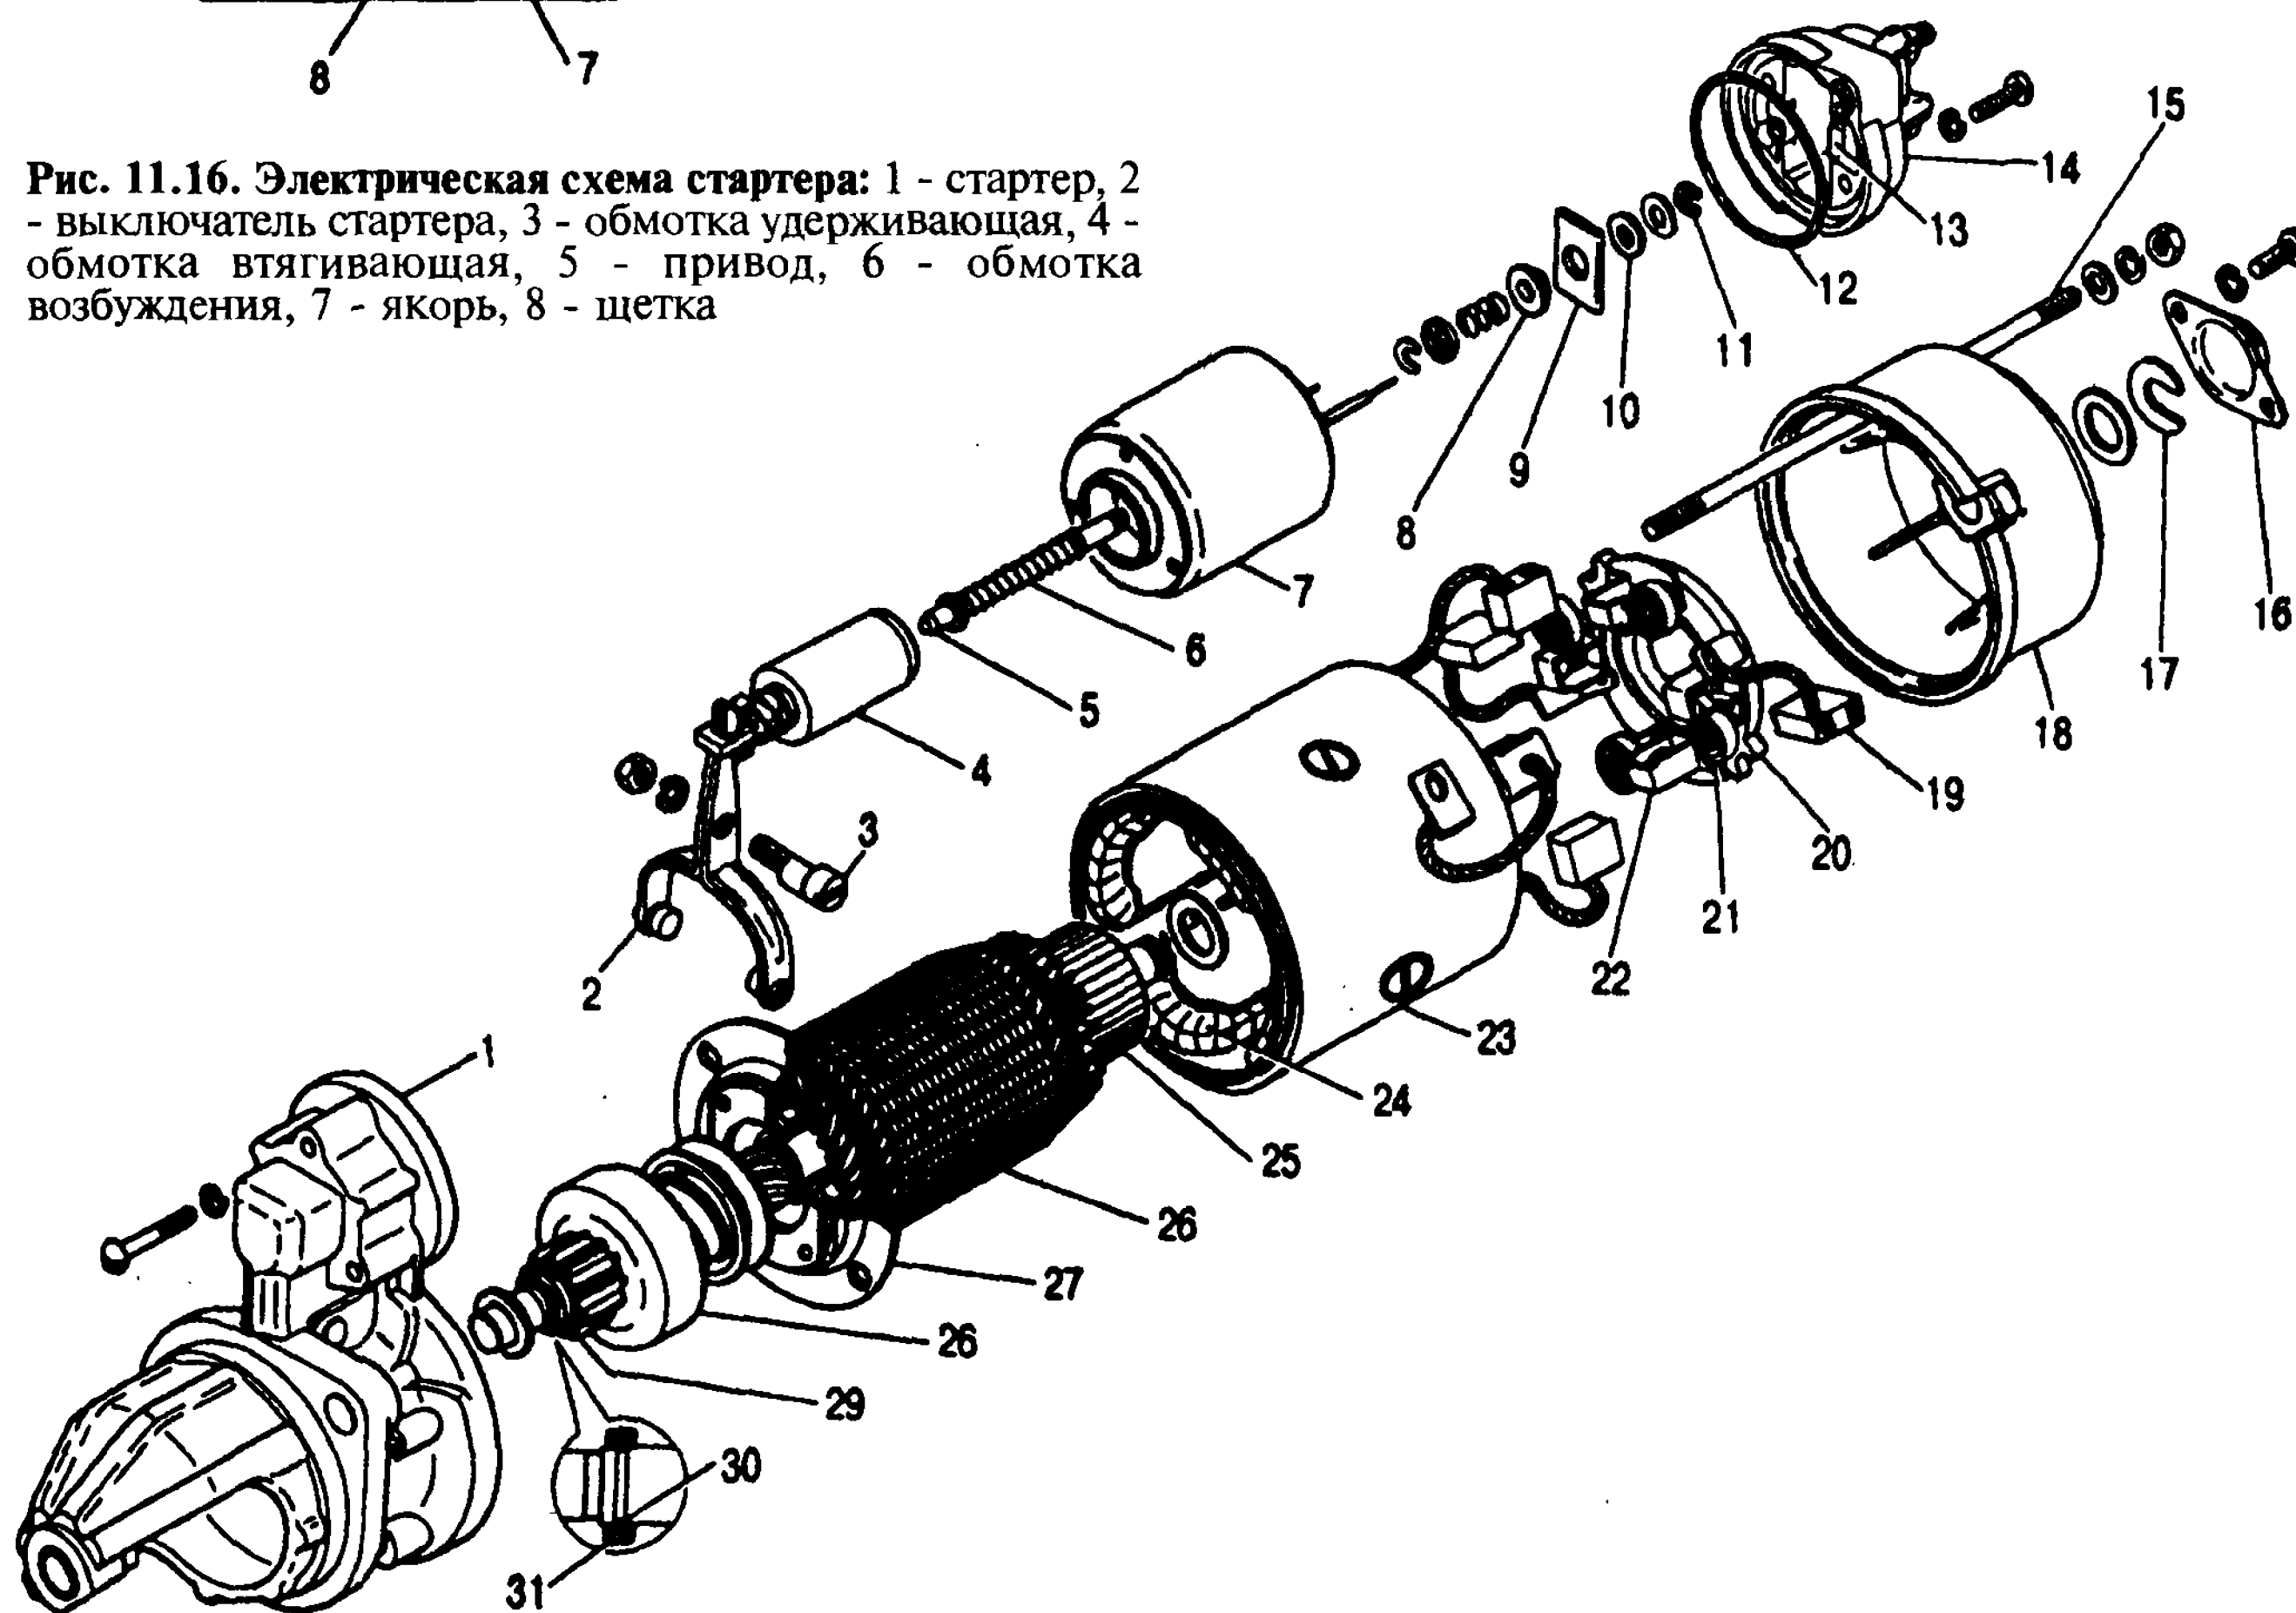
Стартер 42.3708-10: 1 - крышка со стороны привода, 2 - рычаг, 3 - ось рычага, 4 - сердечник тягового реле, 5 - шток тягового реле, 6 - пружина возвратная, 7 - реле тяговое, 8 и 10 - втулки изоляционные, 9 - пластина контактная, 11 и 17 - шайба запорная, 12 - кольцо уплотнительное, 13 - болт контактный, 14 - крышка тягового реле, 15 - шпилька стяжная, 16 - колпак защитный, 18 - крышка со стороны коллектора, 19 - щетка, 20 - держатель щеток, 21 - пружина щетки, 22 - щеткодержатель, 23 - корпус, 24 - обмотка возбуждения, 25 - коллектор, 26 - якорь, 27 - опора промежуточная, 28 - привод с роликовой муфтой свободного хода, 29 - шестерня, 30 - кольцо пружинное, 31 - втулка упорная
